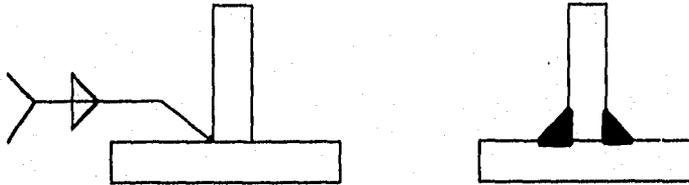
Aplicación de la soldadura por ambos lados.
